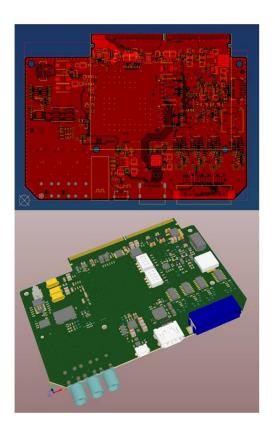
Diseño de la PCB: 2D (arriba) y 3D (abajo).
